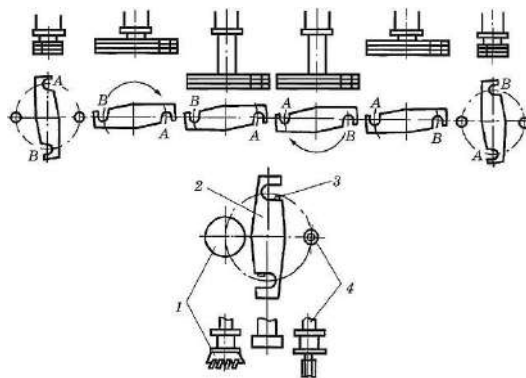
Схема роботи двозахоплювального автооператора [14]
